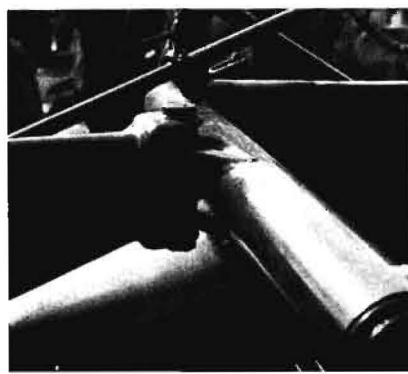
Schwenkbarer Arm an einem Querrohr. Vor das Hohlprofil des Armes ist ein Preßstück als Gabel geschweißt. Das Lager des Drehzapfens wird durch zwei Preßstücke, die am Querrohr verschweißt sind, gehalten
